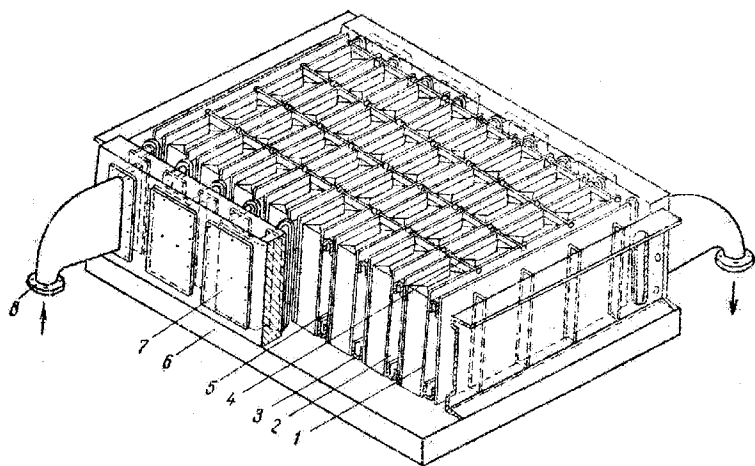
Мембранний морозильний апарат: 1 – гумова манжета; 2 – мембранна камера; 3 – обмежувач; 4 – блок м'яса; 5 – сталева мембрана; 6 – рухоме дно; 7 – колектор; 8 – патрубок для холодоносія.
